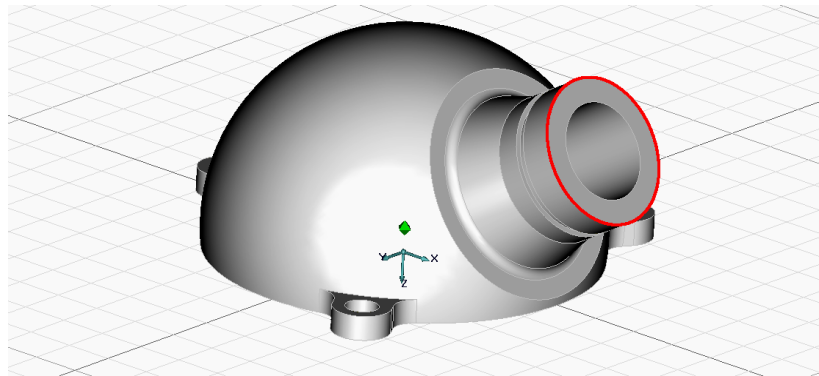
Місце створення фаски на циліндричній частині деталі
